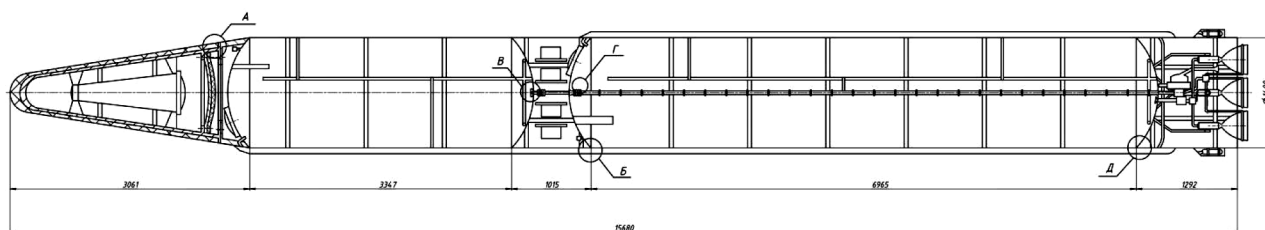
Чертеж одноступенчатой баллистической ракеты
